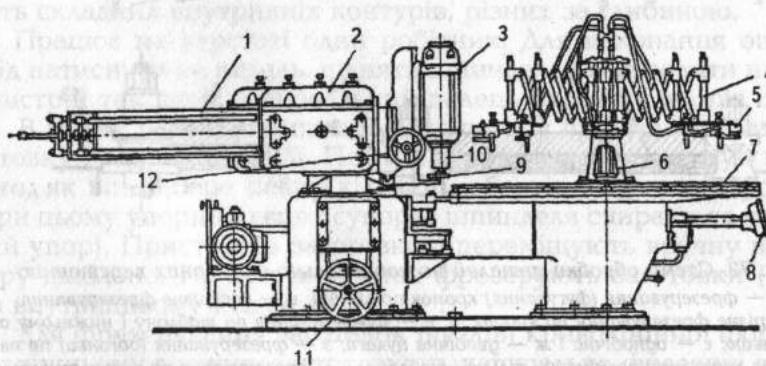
Двошпиндельний карусельно-фрезерний верстат Ф2К-2:
